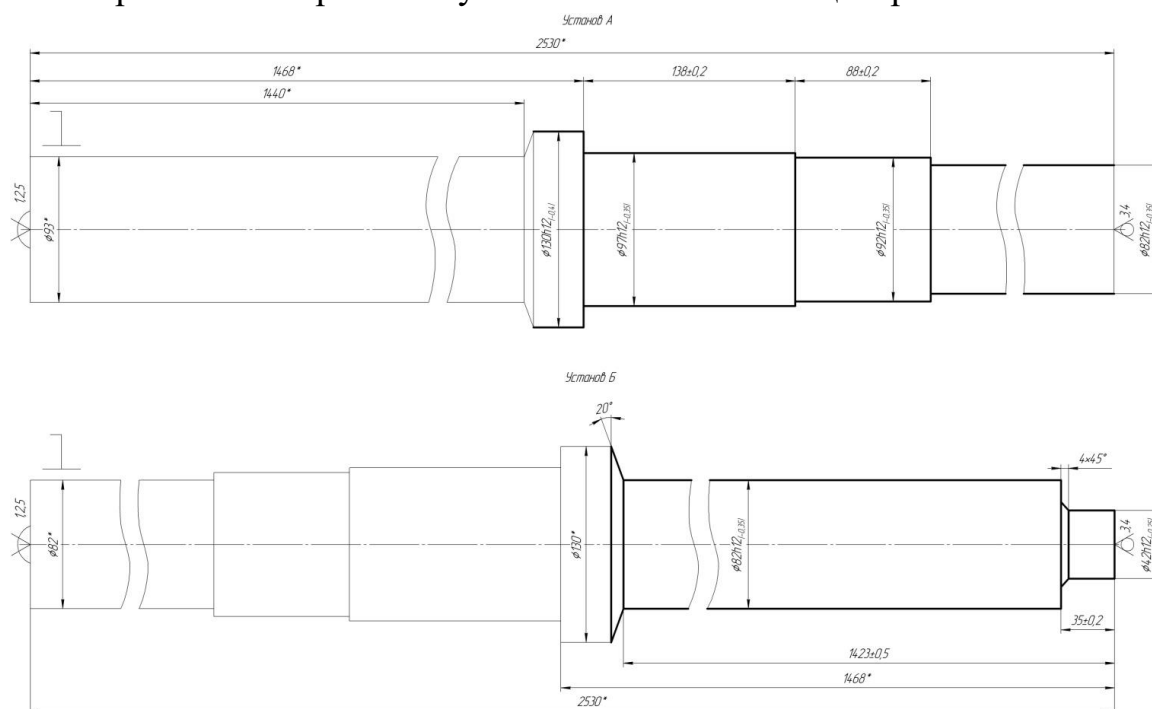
Схема базування заготовки на токарній з ЧПК операції (перший варіант)
